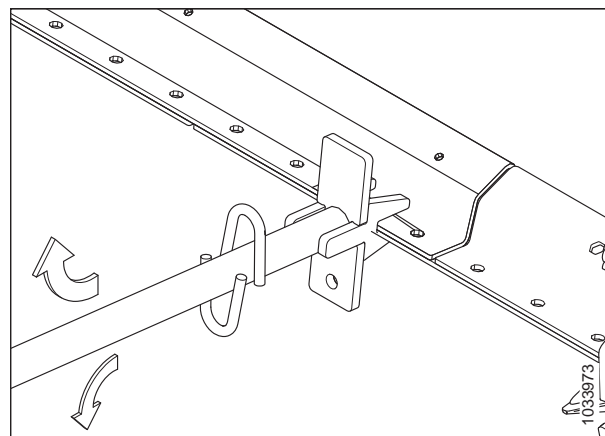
Регулировка пальцевого бруса — без противорежущих пальцев
